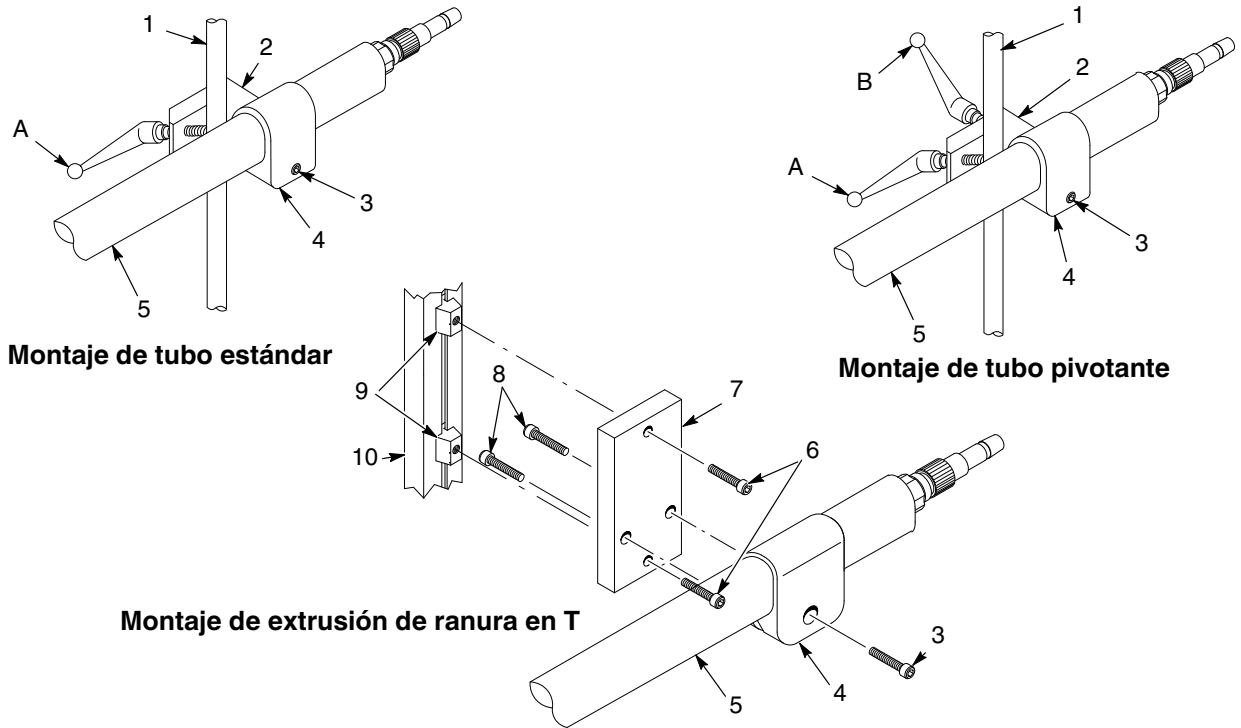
Conjuntos de montaje de la pistola de montaje en tubo
